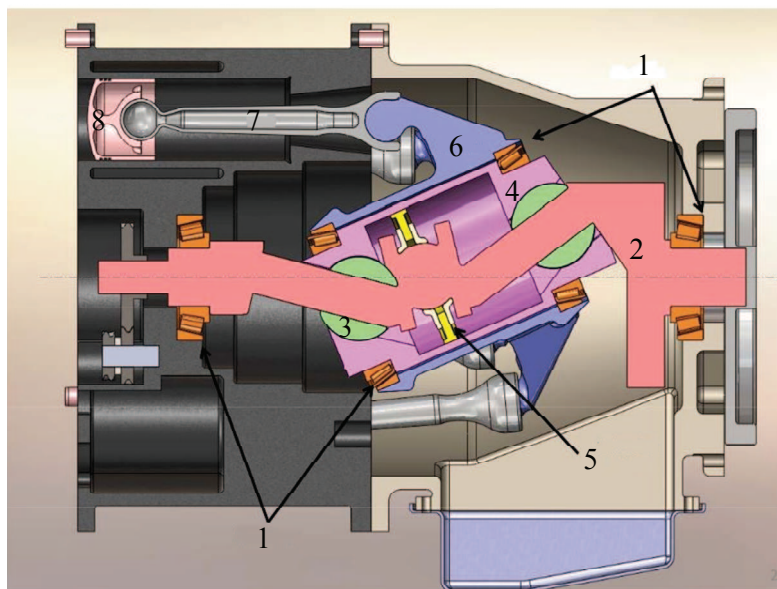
Двигун з безступінчастою зміною робочого об'єму: 1 – підшипник; 2 – колінчастий вал; 3 – втулка; 4 – муфта; 5 – активний поршень; 6 – тримаюча корона; 7 – шатун; 8 – поршень
